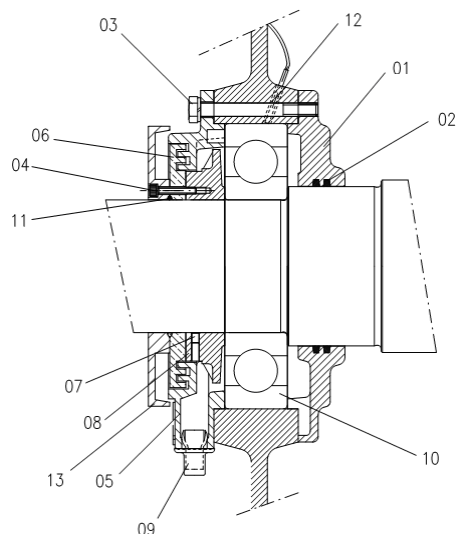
Детали подшипника качения на смазочном веществе
